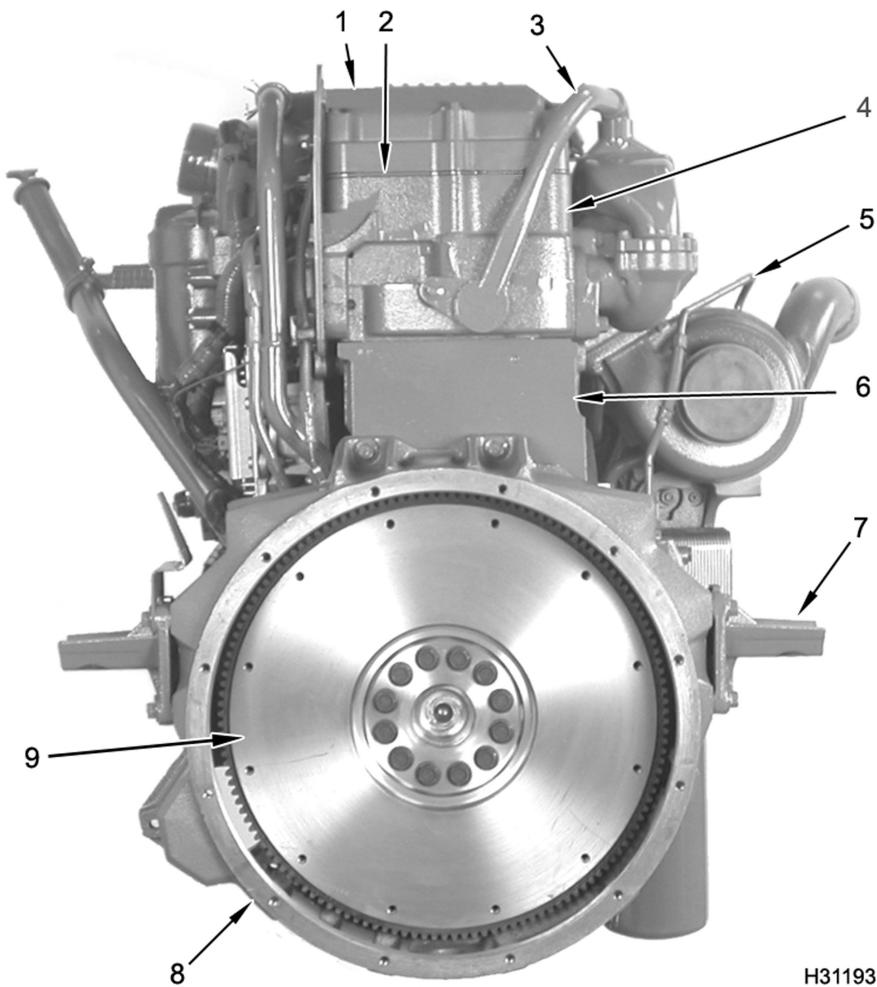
Ubicación de los componentes mecánicos (vista desde la izquierda)
